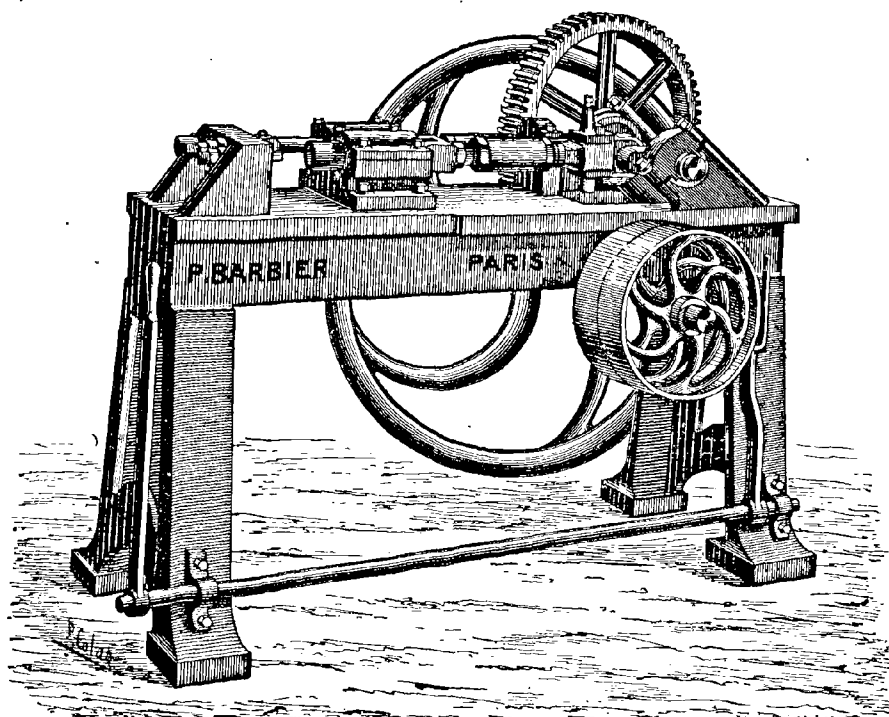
Machine horizontale à emboutir de M. Barbier.
